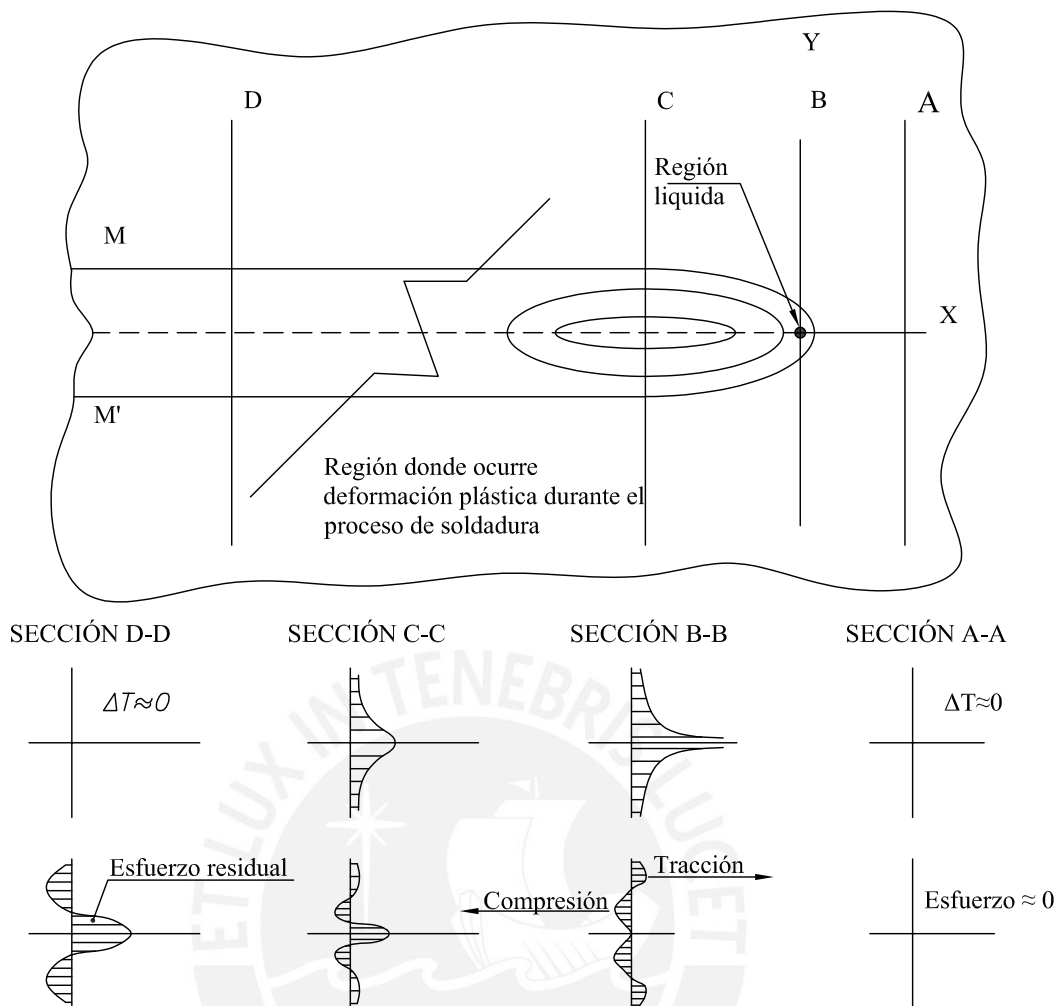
Estados transitorios y finales durante la soldadura (Masubushi, 1982).
